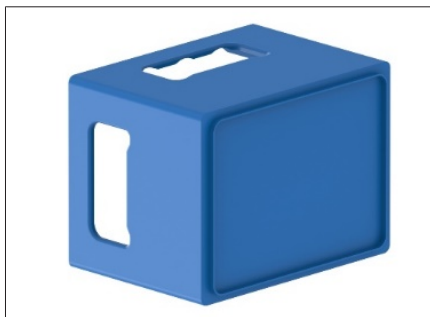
Geometria de encaixe comum para empilhamento em colunas
